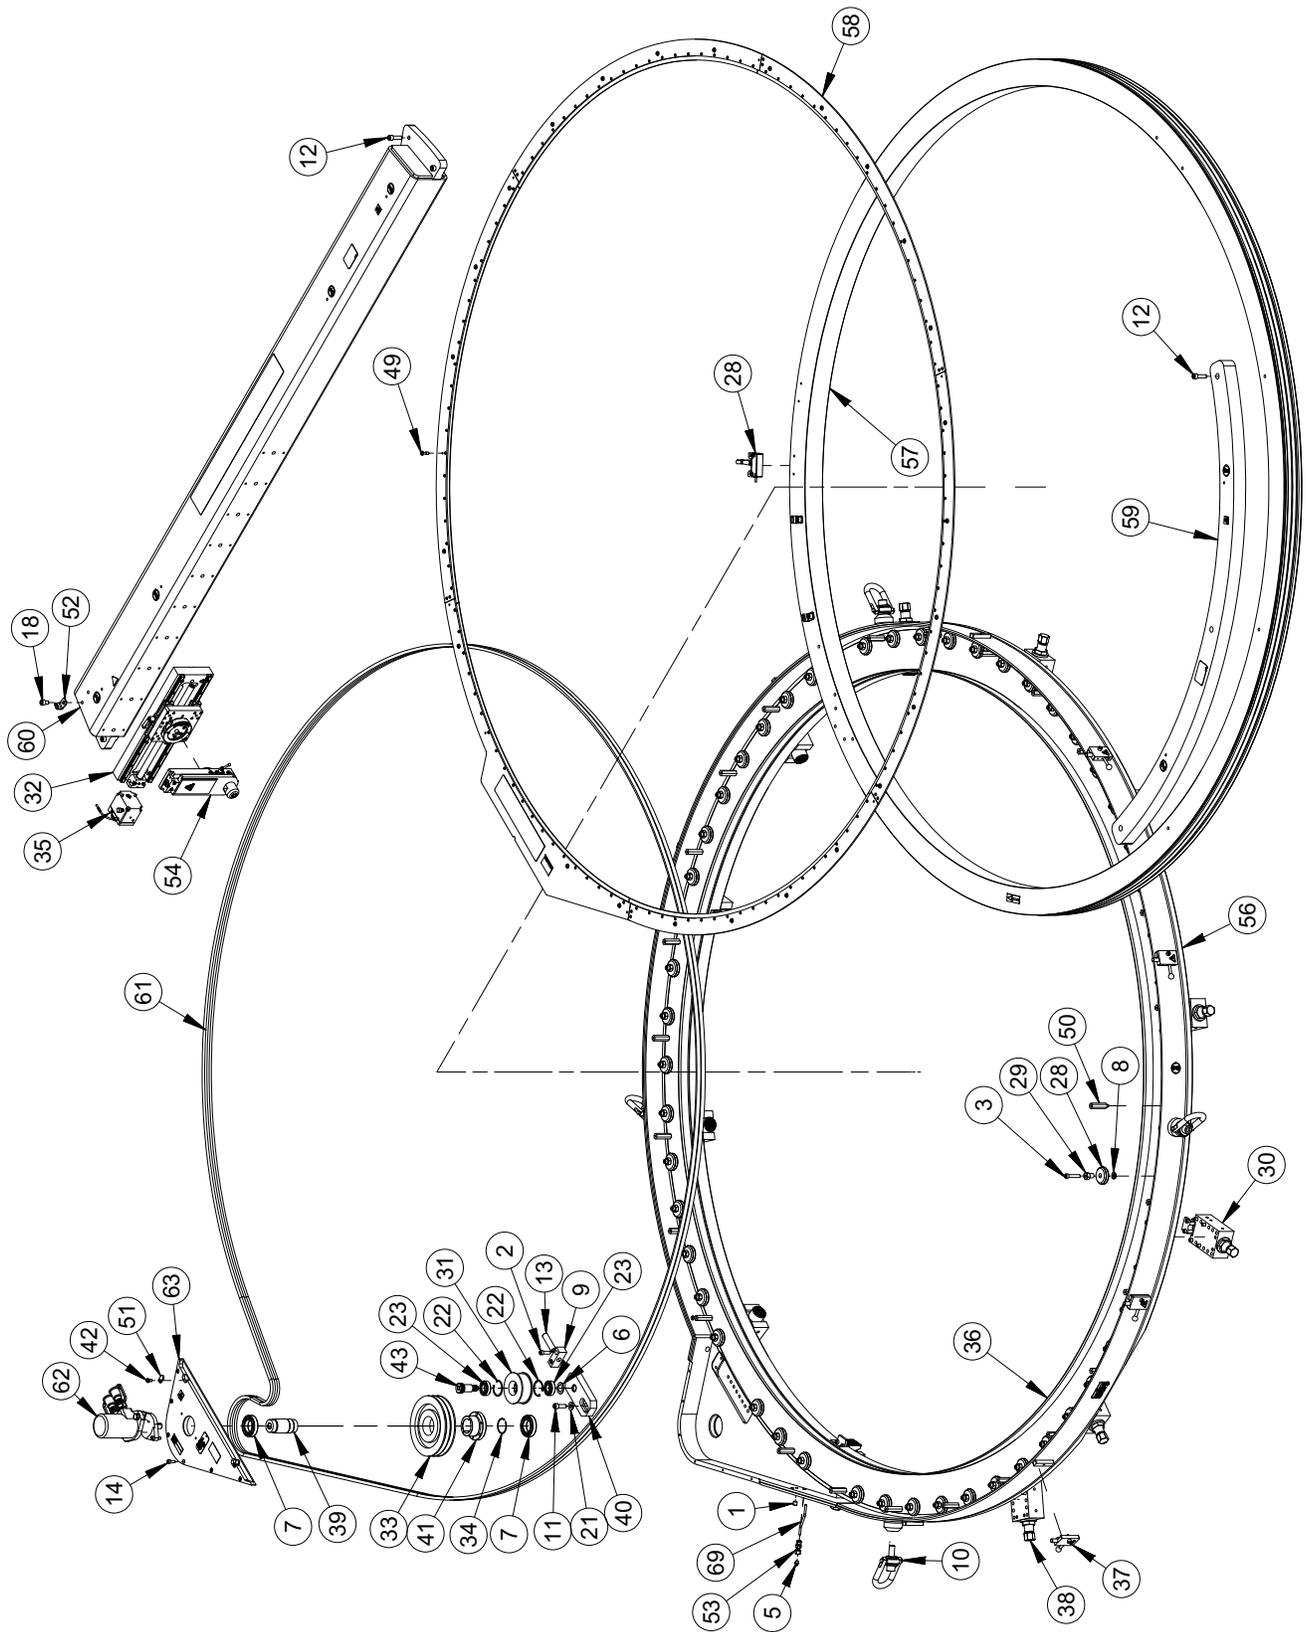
ODF110 SPEED FACER ENSEMBLE 1 (RÉF. 7639-S2)
